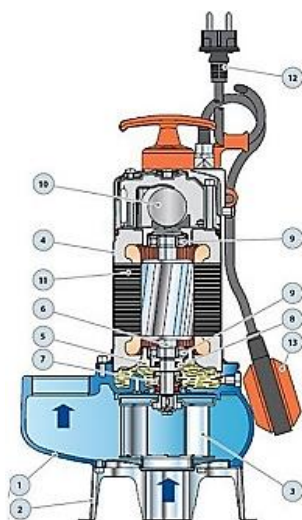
Принципиальная схема погружного центробежного дренажного насоса с вертикальной компоновкой вала электродвигателя [4]: 1 – корпус насоса, 2 – основание, 3 – рабочее колесо, 4 – крепление электродвигателя, 5 – крышка электродвигателя, 6 – ведущий вал, 7 – двойное уплотнение вала в масляной камере, 8 – сальник, 9 – подшипники, 10 – конденсатор, 11 – электродвигатель, 12 – кабель электропитания, 13 – внешний поплавковый выключатель
